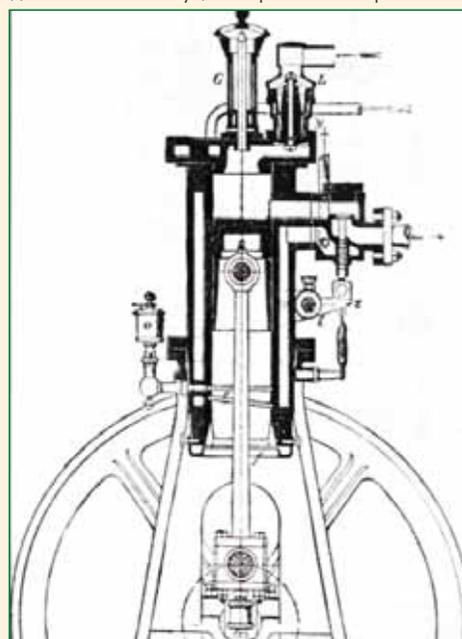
"Безопасный" двигатель Б.Г. Луцкого (рисунок взят из книги Ф. Засса): a, b, c - трубопровод подачи бензина; d - впускной клапан; e - отверстия для подачи бензина к воздуху; f - калильная трубка; g - подогрев калильной трубки; h - трубопровод подачи воздуха; i - трубопровод подачи охлаждающей воды; k - выпускной клапан
